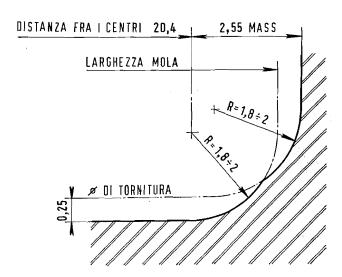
Raccordi da eseguire sugli spallamenti di biella.
